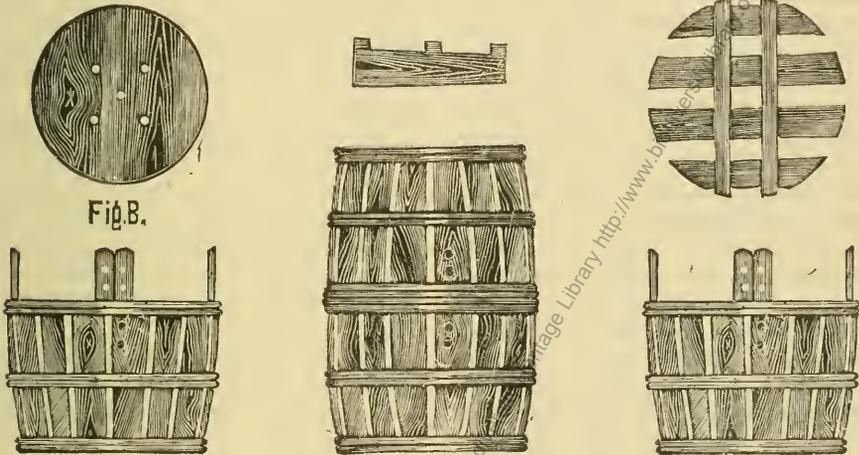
Theilbares Obstaufbewahrungs- und Versandfass.
